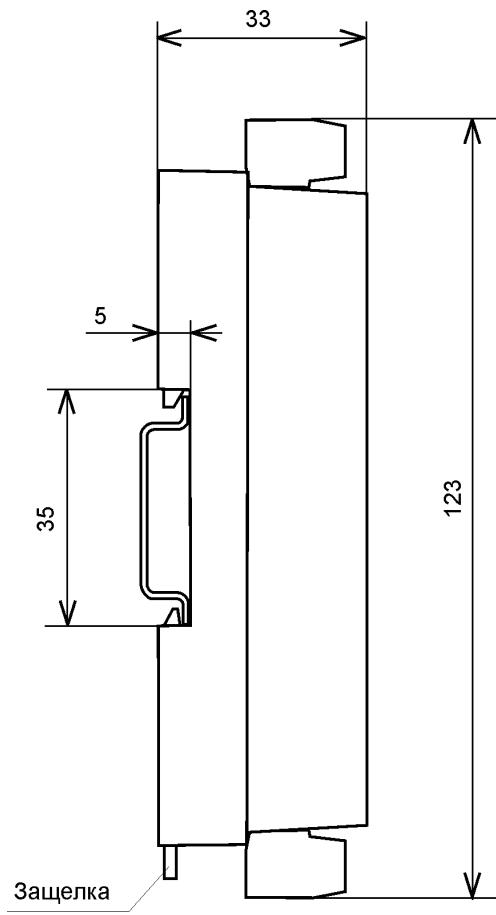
Габаритный чертеж модуля с креплением к DIN-рейке. Вид сбоку.
